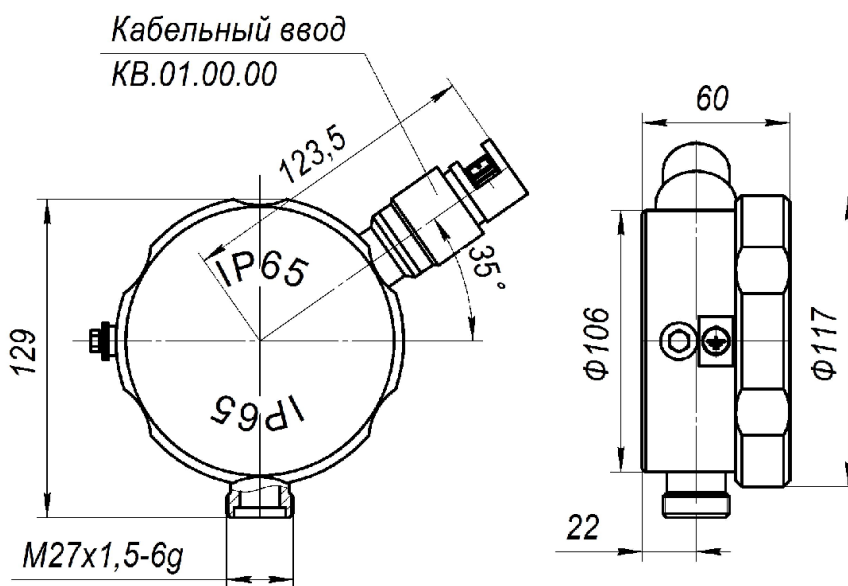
Габаритные и монтажные размеры рН-метра рН-4101
